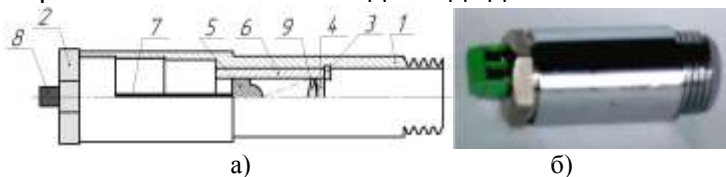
Конструкція (а) та зовнішній вигляд (б) датчика фронту та спалаху полум'я: 1 – корпус; 2 – кришка; 3 – кільце стопорне; 4 – світлофільтр; 5 – фотодіод; 6 – втулка; 7 – плата друкована; 8 – клемник; 9 – об'єктив
